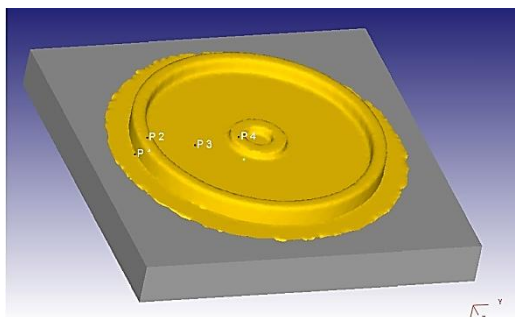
Зображення поковки та нанесеними на неї чотирма точками
